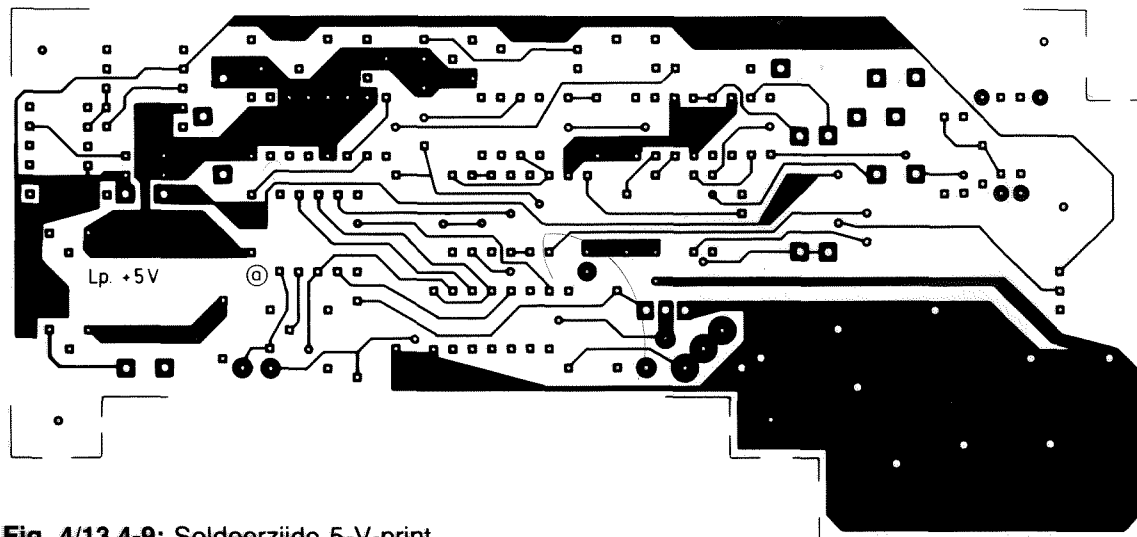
/13.4-9: Soldeerzijde 5-V-print.
